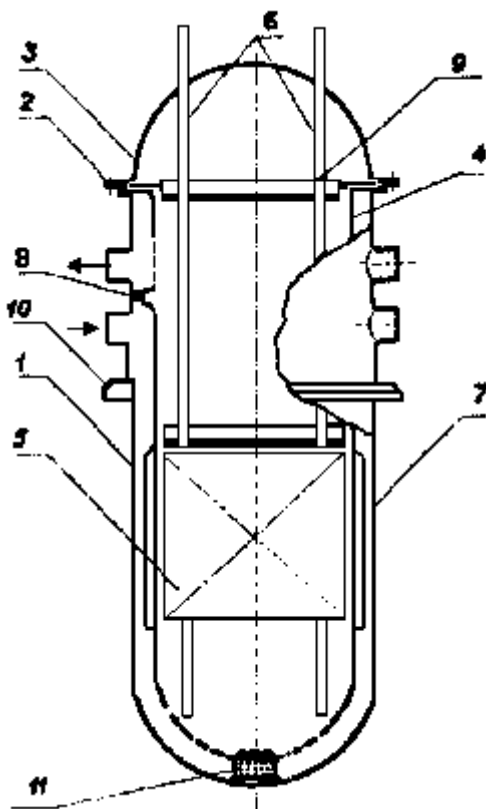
Принципова конструктивна схема реактора ВВЕР
